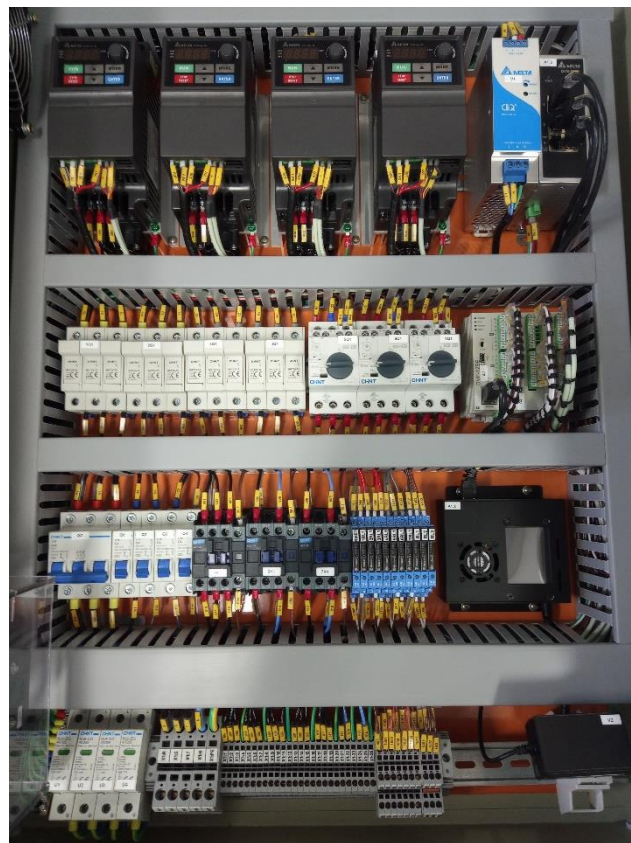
Placa de montagem da empacotadora com minicomputador já implementado
